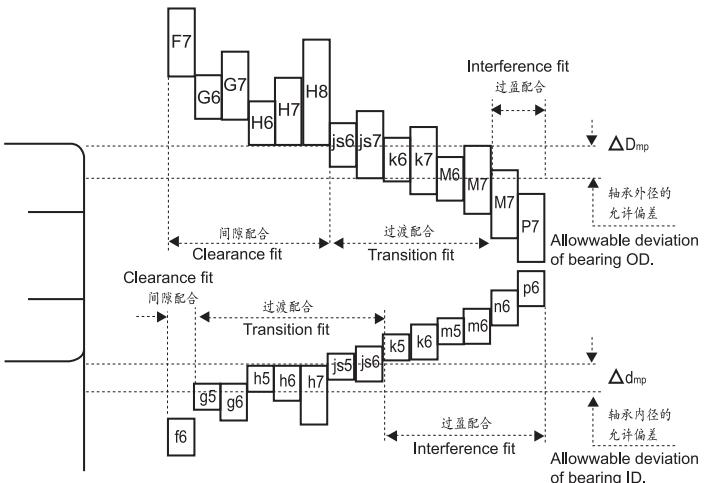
轴和外壳孔的尺寸公差与配合的关系 (0级公差的轴承)
